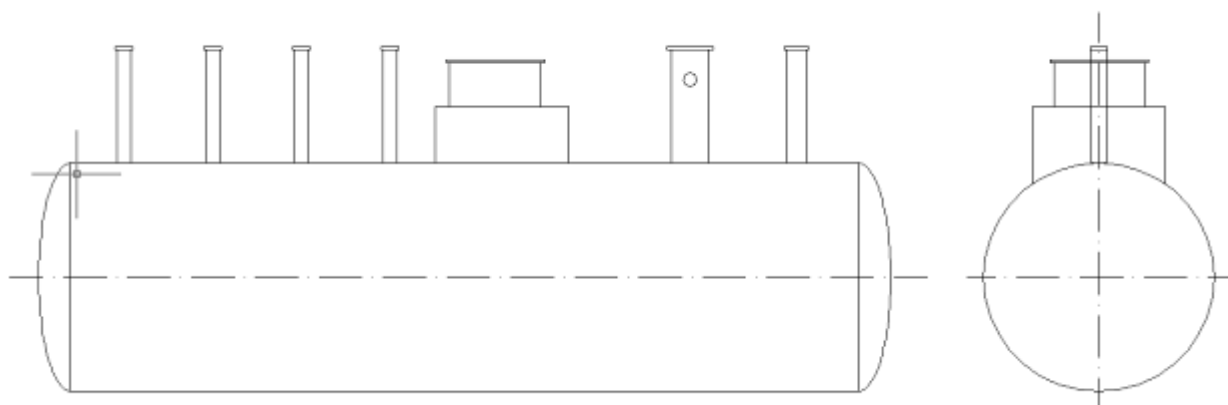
Эскиз общего вида резервуара РГС-50
